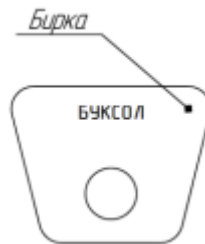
Бирка буксового узла с подшипниками роликовыми цилиндрического, заправленного смазкой Буксол или ЗУМ
